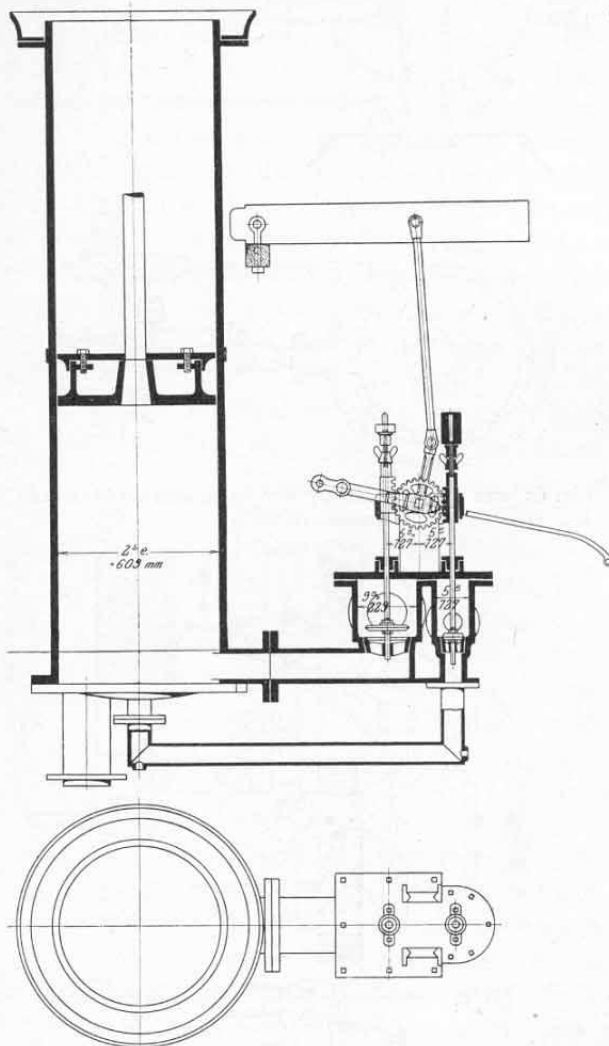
und 69. Zylinder und Steuerung einer deutschen atm. Maschine um 1800.
